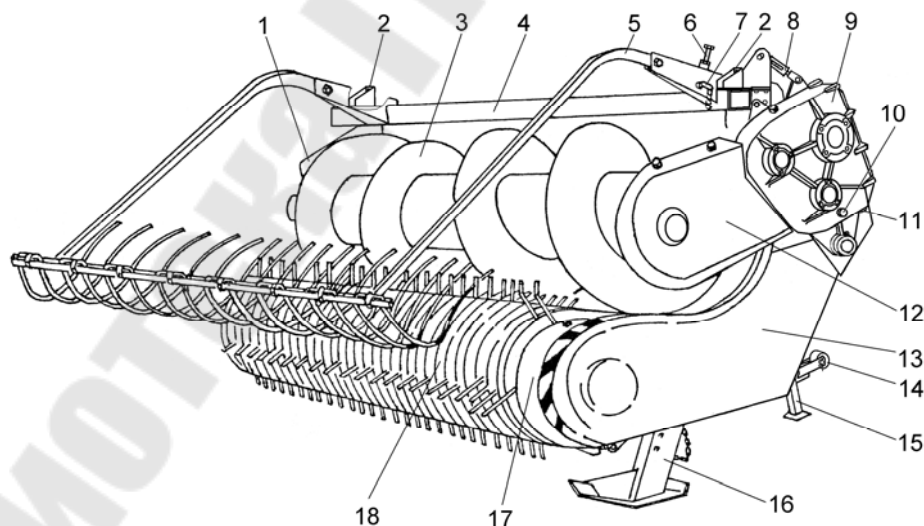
Подборщик: 1 – рычаг правый; 2 – кронштейны; 3 – шнек; 4 – рама; 5 – устройство прижимное; 6 – болт регулировочный; 7 – фиксатор; 8 – стяжка; 9 – редуктор; 10 – пробка контрольная; 11 – пробка сливная; 12 – крышка рычага; 13 – ограждение; 14 – ловитель нижний; 15 – стояночная опора; 16 – башмак; 17 – стяжка; 18 – устройство подбирающее
